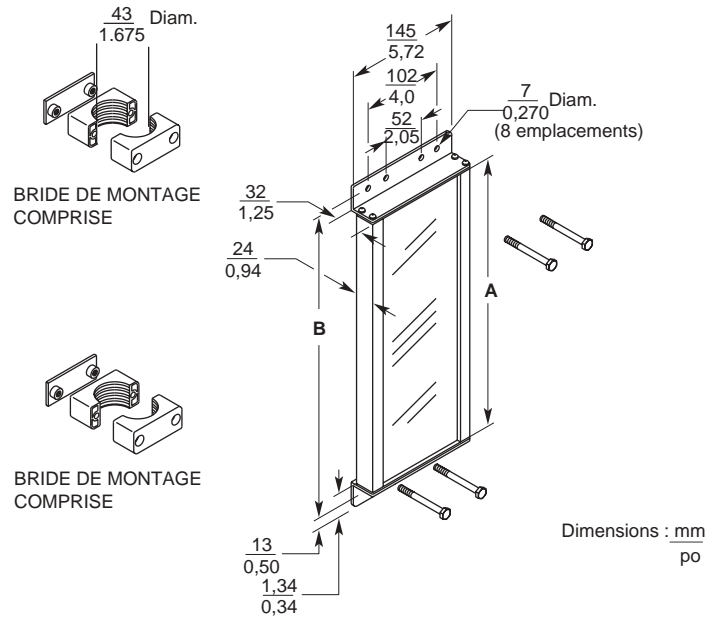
Dimensions des miroirs (voir le Tableau 28 pour les dimensions A et B)
